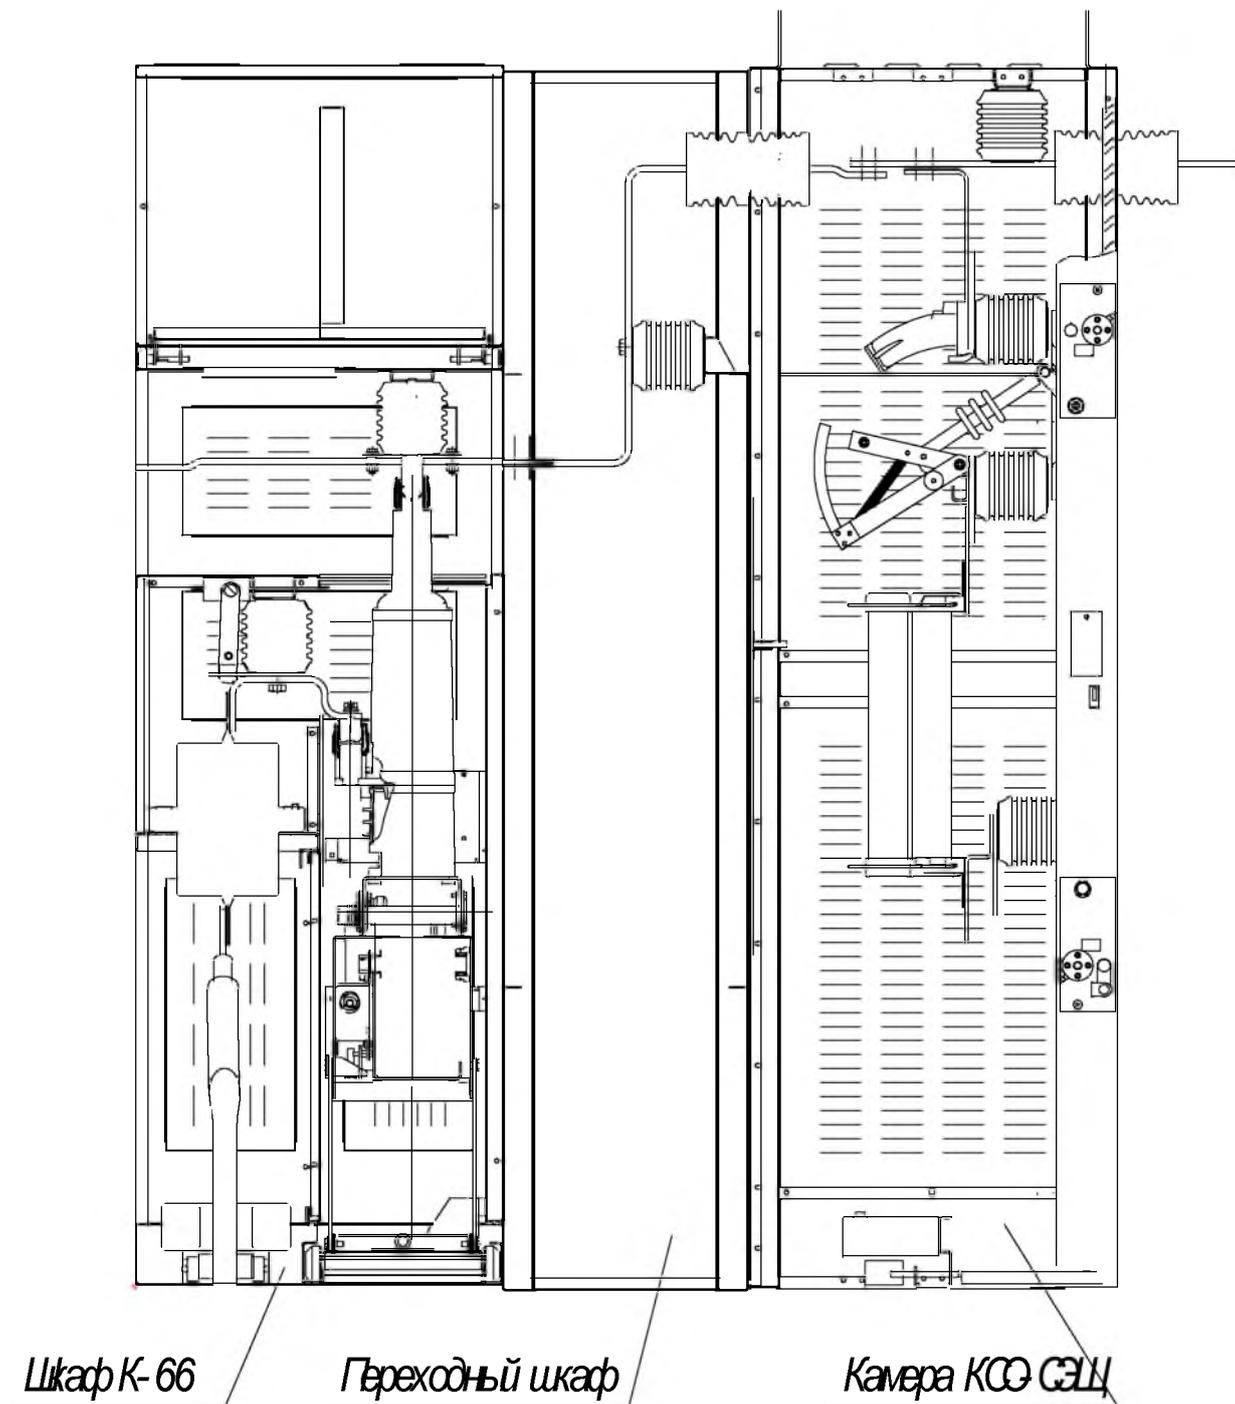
Стыковка камер КСО-СЭЦ с шкафами КРУ СЭЦ-66
